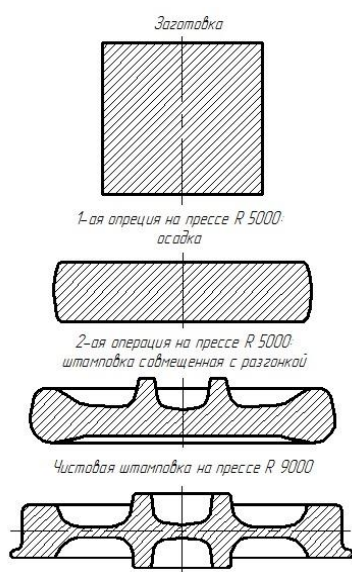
Схема черновой и чистовой штамповки по предложенному способу
